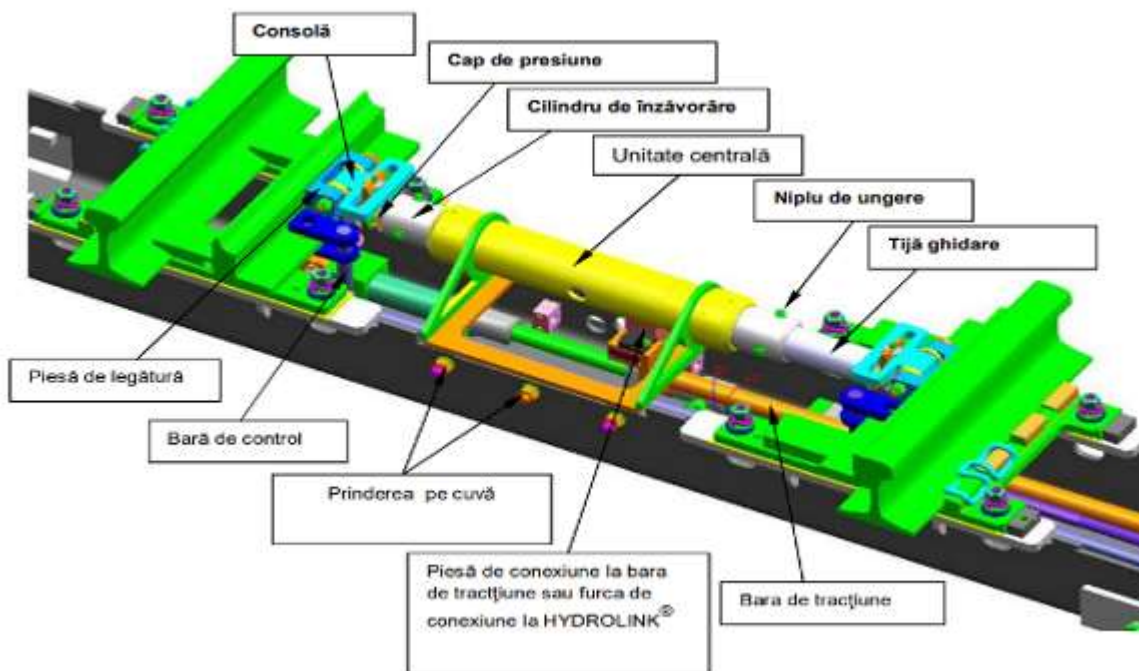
Descrierea elementelor componente (sursa: Instrucțiuni de montaj, exploatare și întreținere fixător tip - SPHEROLOCK® - pentru șină tip 60E1 amplasat în cuvă metalică I 03.04.00-21 rev.0 29.11.2013)
